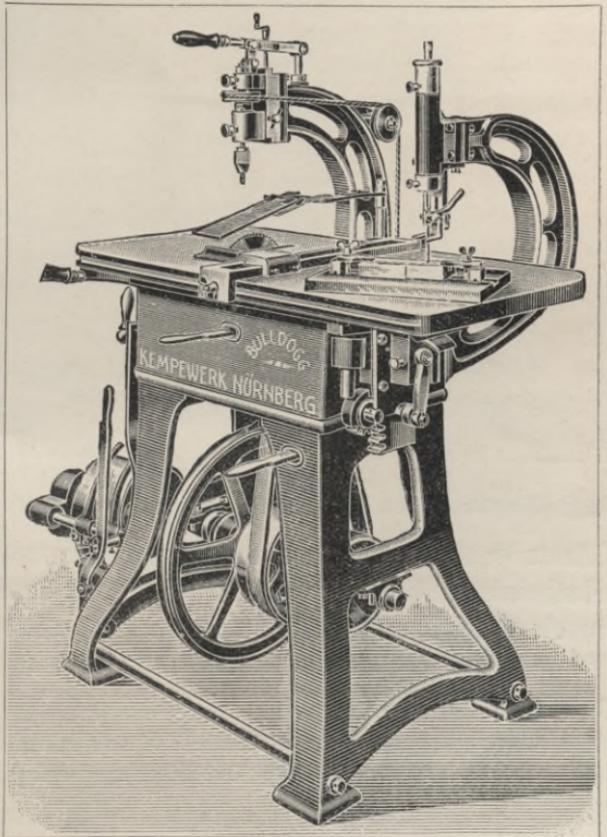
Kombinierte Fräsmaschine „Bulldogg“ in Verbindung mit Kreisäge, Bestoßlade, Bohrmaschine.
